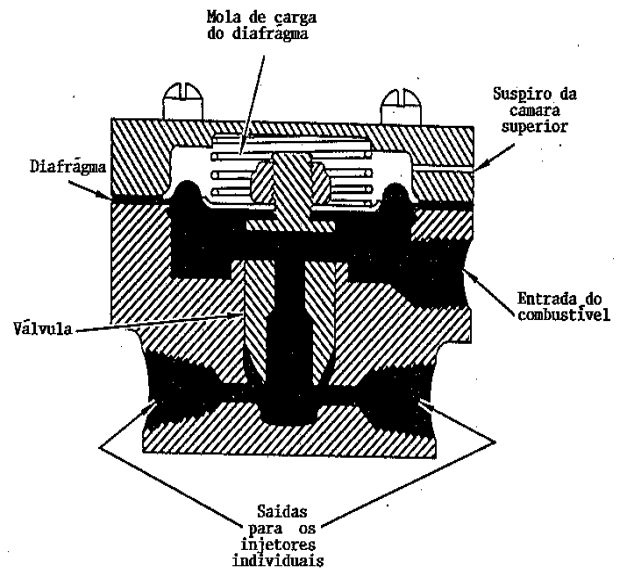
Conjunto da válvula do duto principal de combustível.
